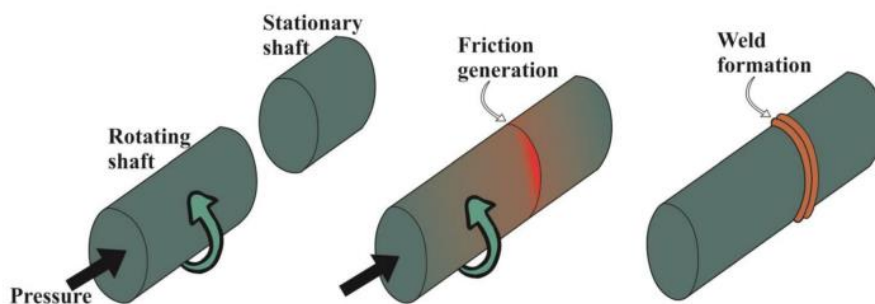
Unión por soldadura por fricción. (44)
